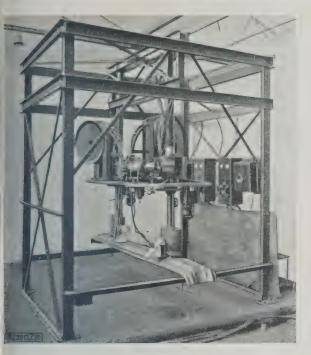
Selbsttätige Schwellenschweißanlage der mit zwei Schweißköpfen zum gleichzeitigen Aufschweißen von Hakenplatten auf eisernen Schwellen.
